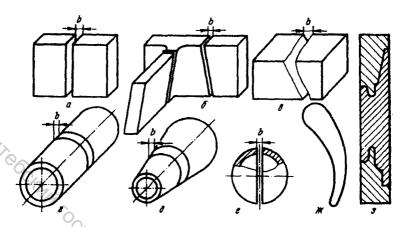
Виды швов, выполняемые электрошлаковой сваркой:
